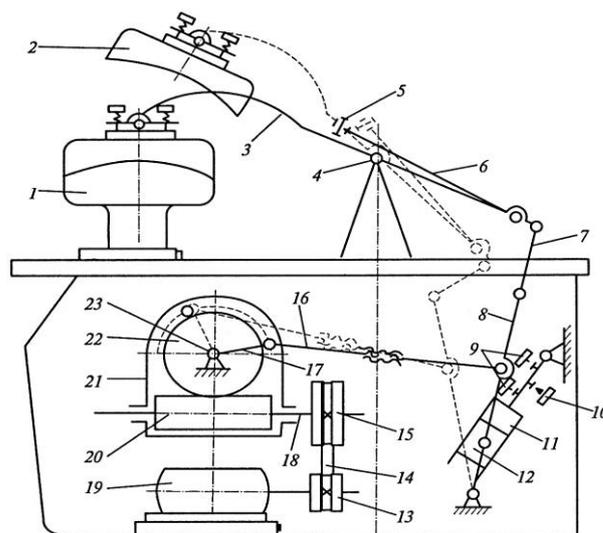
Кинематическая схема механизмов пресса марки Cs-311
